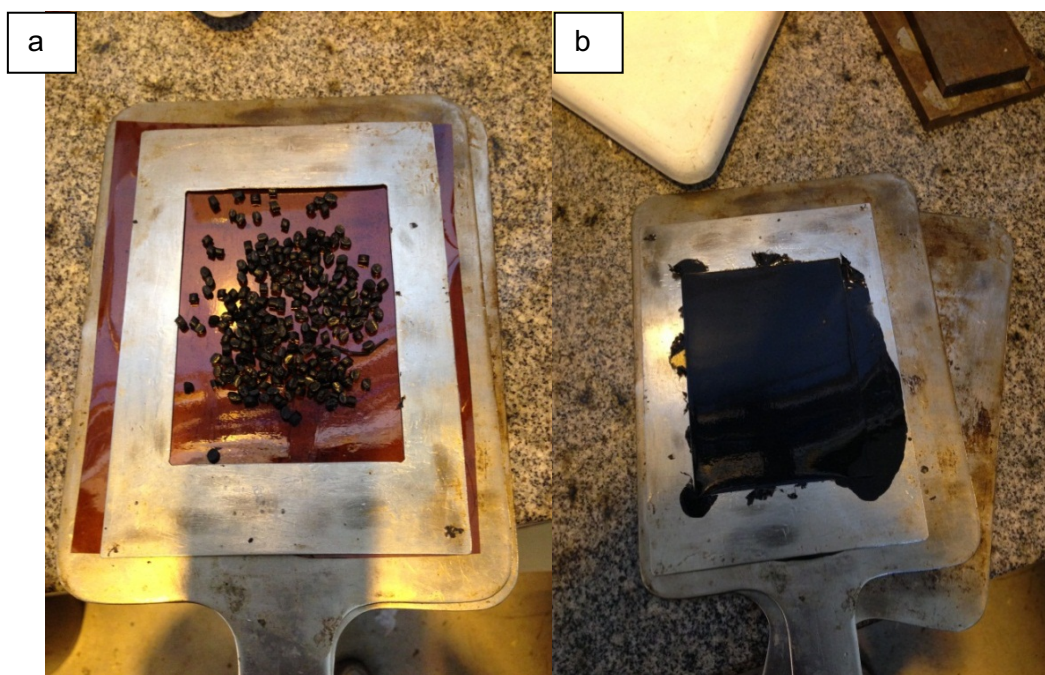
Fotografias do (a) molde com pellets a serem moldados e (b) placa moldada.
